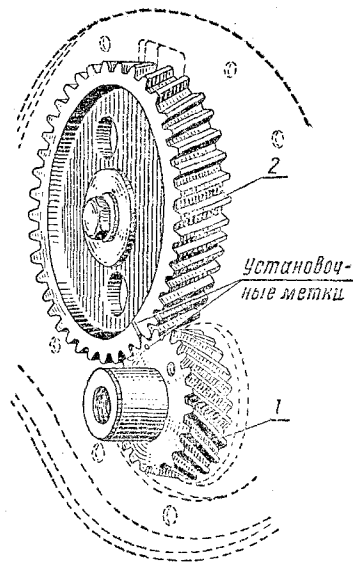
Расположение шестерен распределения двигателя ГАЗ-21А:
